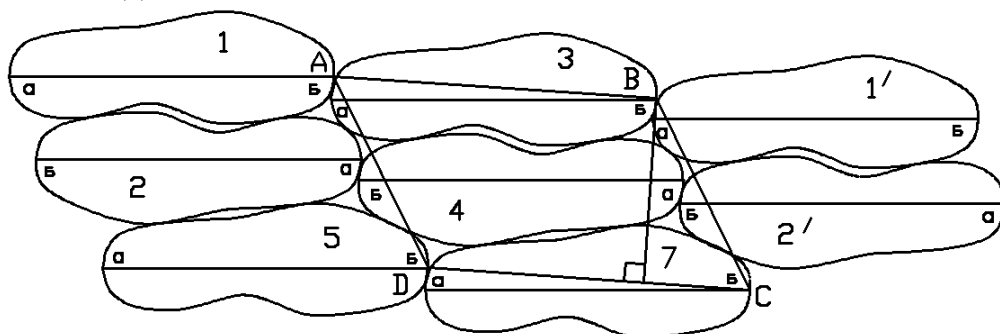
Схема совмещения подошв и стелек в пучках (вариант 1)
